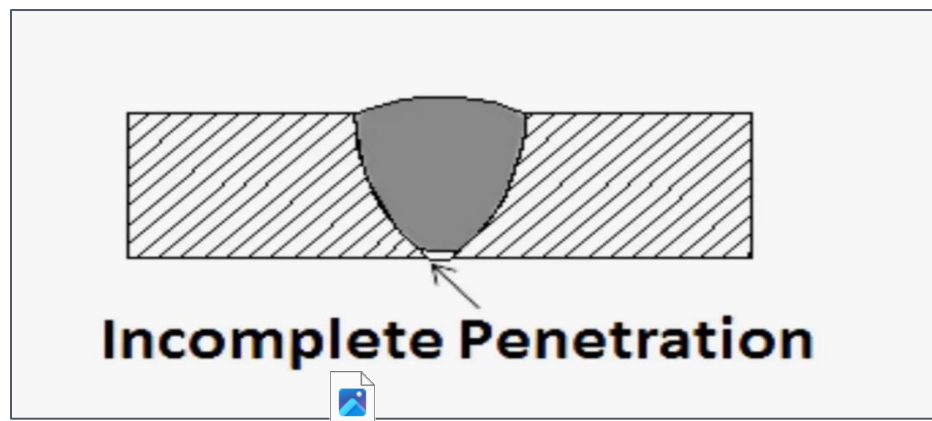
Manque de fusion à la racine de la soudure.
